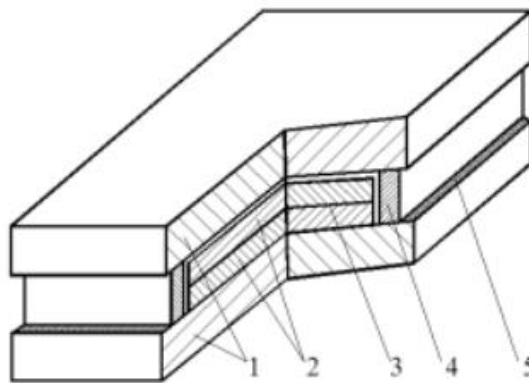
Конструкція чотиришарового біметалічного пакета
